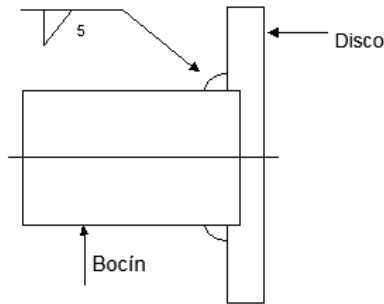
Soldadura de filete (disco y bocín)
